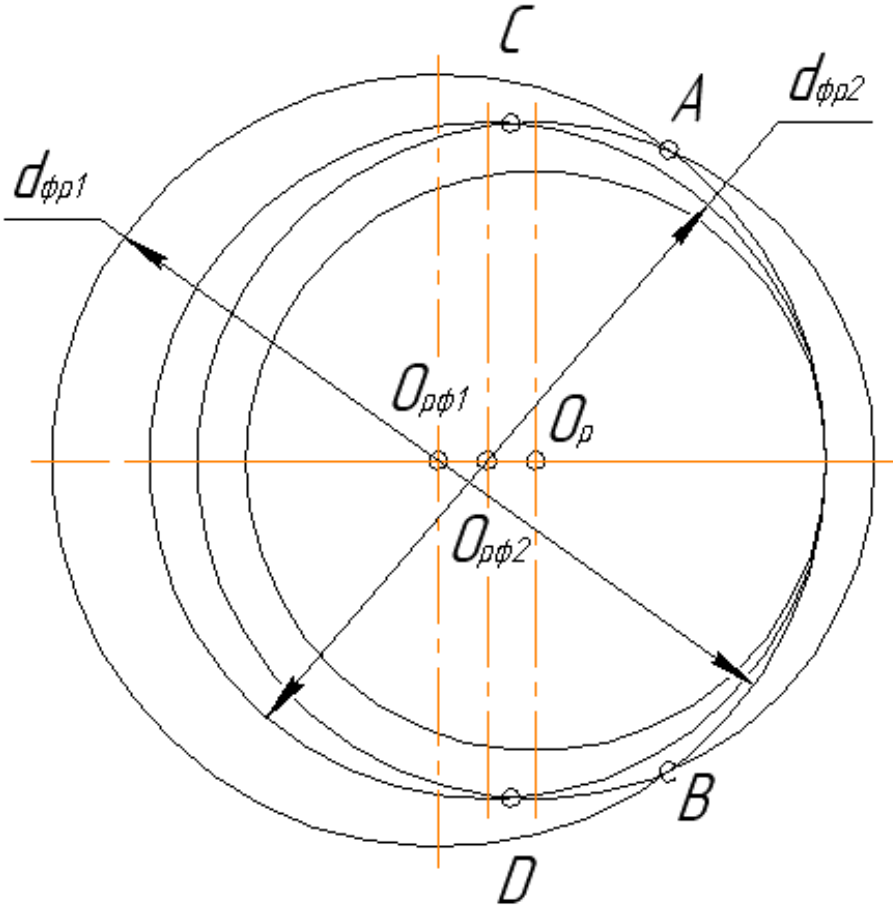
Схема сравнения величины дуги контакта нарезаемой резьбы с инструментами разного диаметра [5, с. 2]
